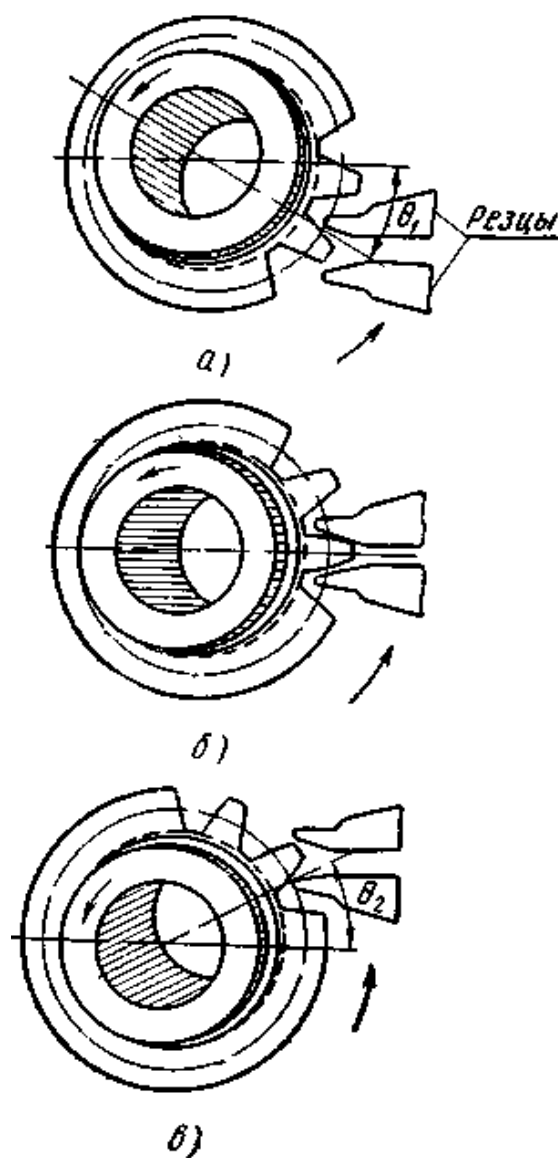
Последовательное положение резцов относительно зубьев нарезаемого колеса при нарезании методом обкатки (а – ниже центра, б – по центру, в – выше центра станка)
